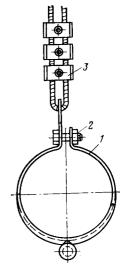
Приспособление для безопасного ирепления промывочного шланга:
